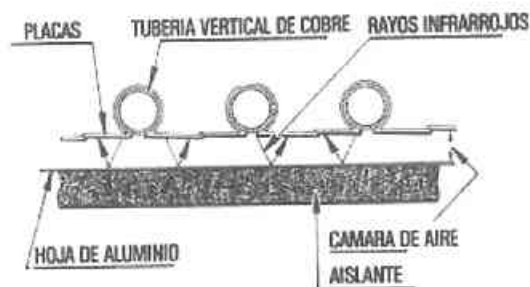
La placa absorbente está integrada por placas más pequeñas, soldadas entre sí y que envuelven a los conductos del circuito.
